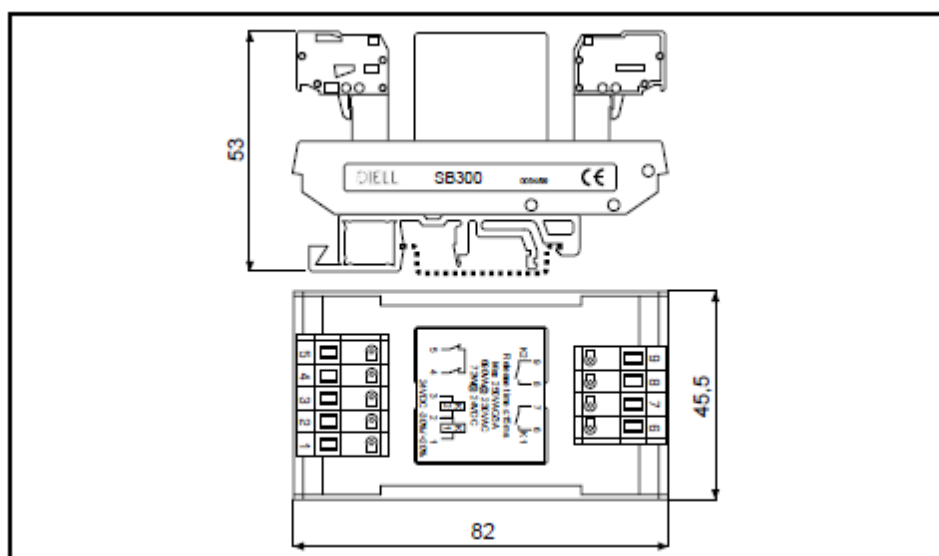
Dimensioni meccaniche del modulo a relé SB300
